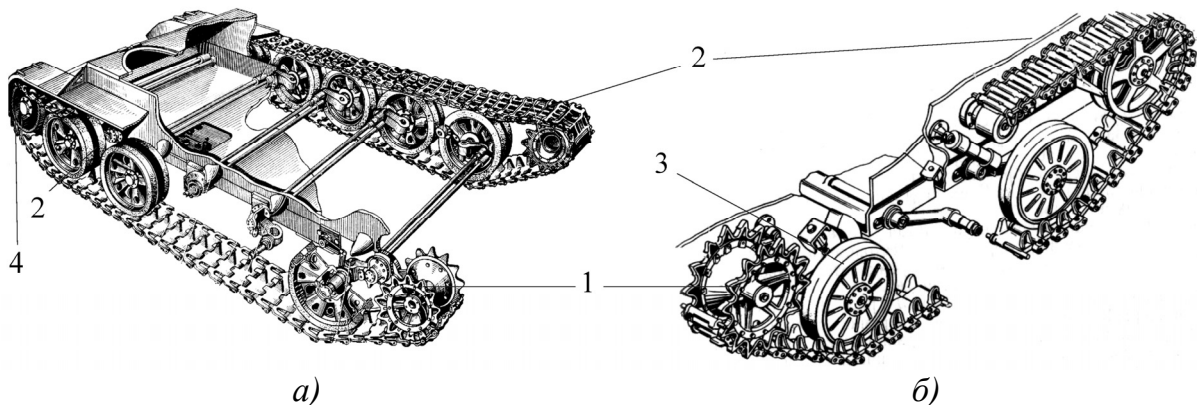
Гусеничный движитель: 1 – ведущее колесо; 2 – гусеница; 3 – опорные катки; 4 – направляющее колесо
